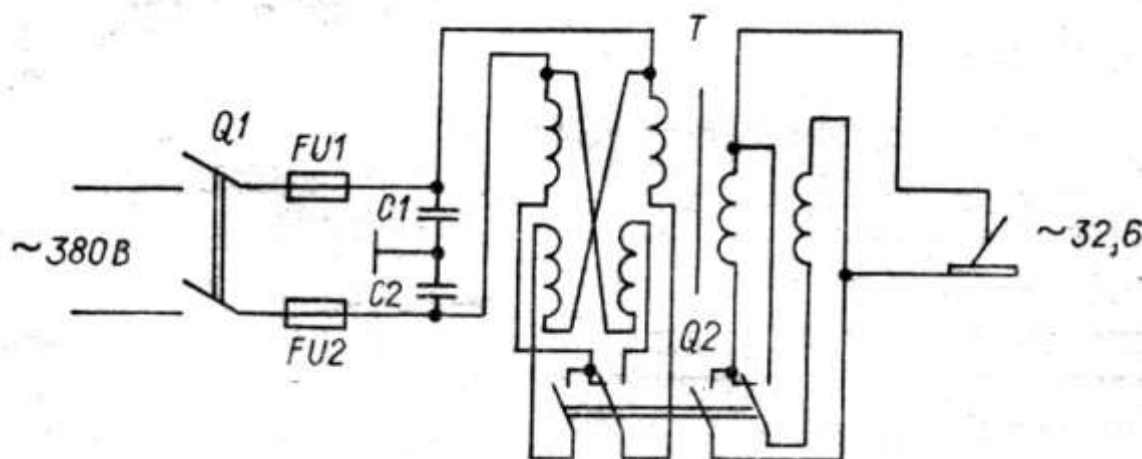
Принципова електрична схема зварювального трансформатора ТД-306
